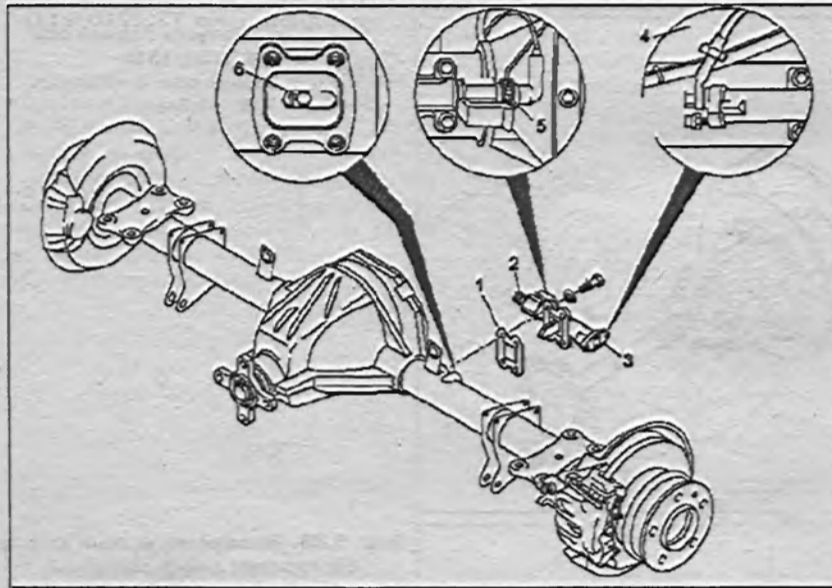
Снятие и установка цилиндра включения блокировки дифференциала:
